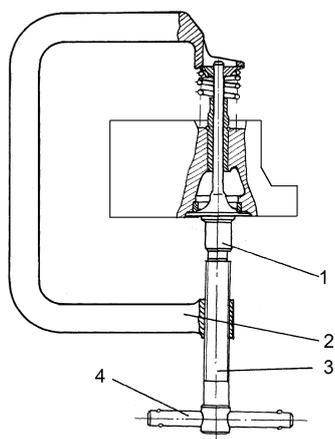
Установка пружин клапанов с помощью универсального приспособления:
